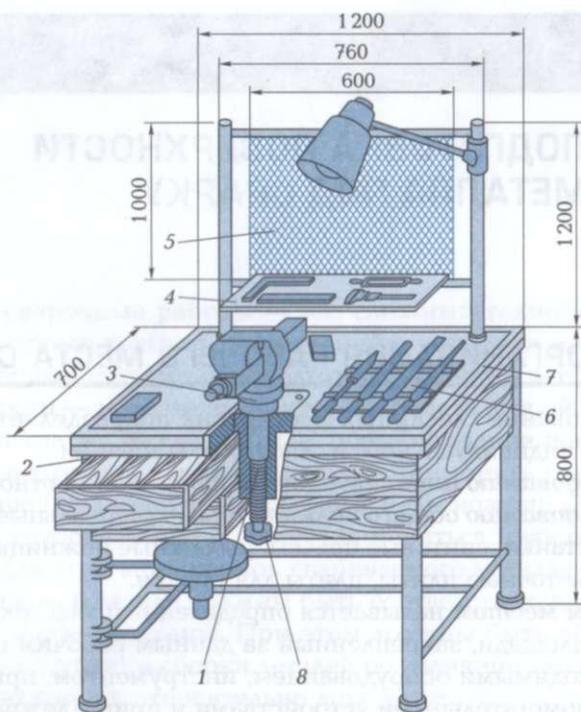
Слесарный верстак с регулируемыми по высоте тисками:
